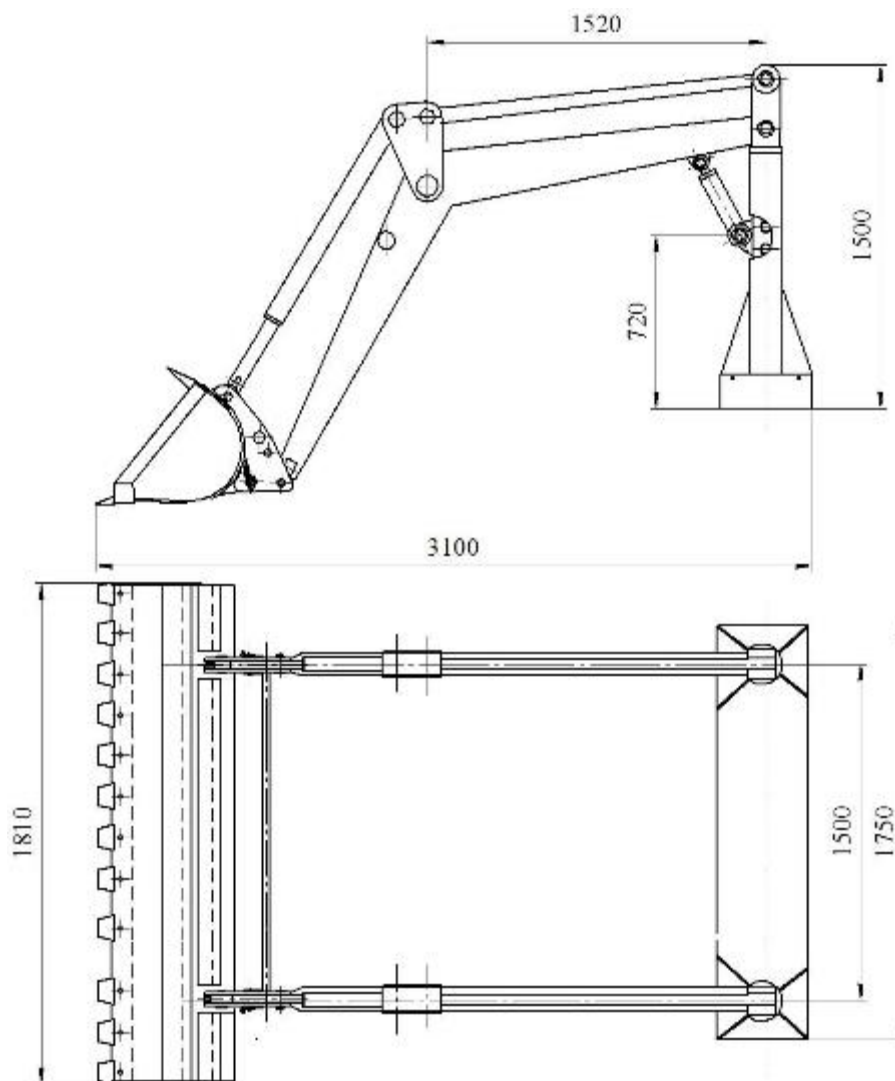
Принципова схема поворотного механізму фронтального навантажувача
